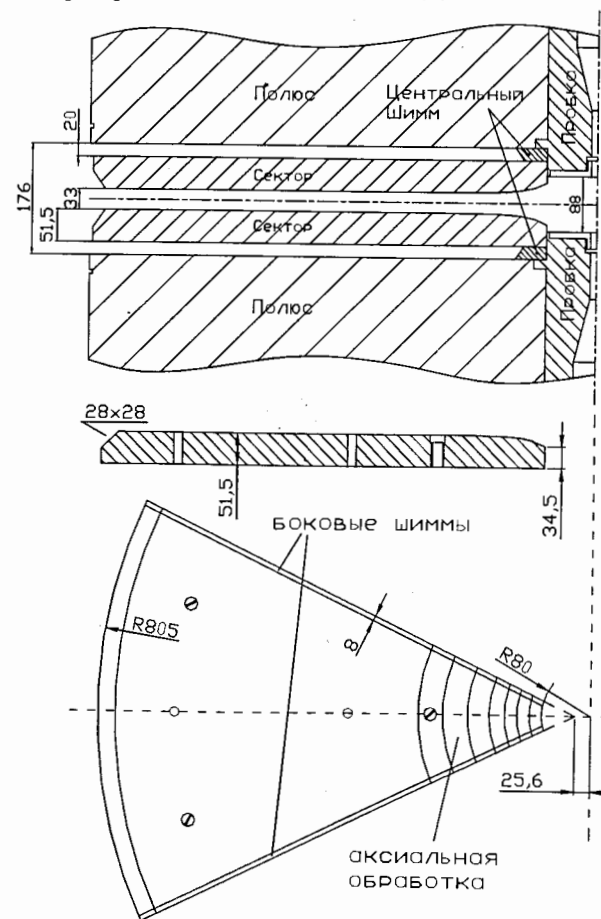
Размеры межполюсного зазора. Форма и основные размеры секторной сборки
